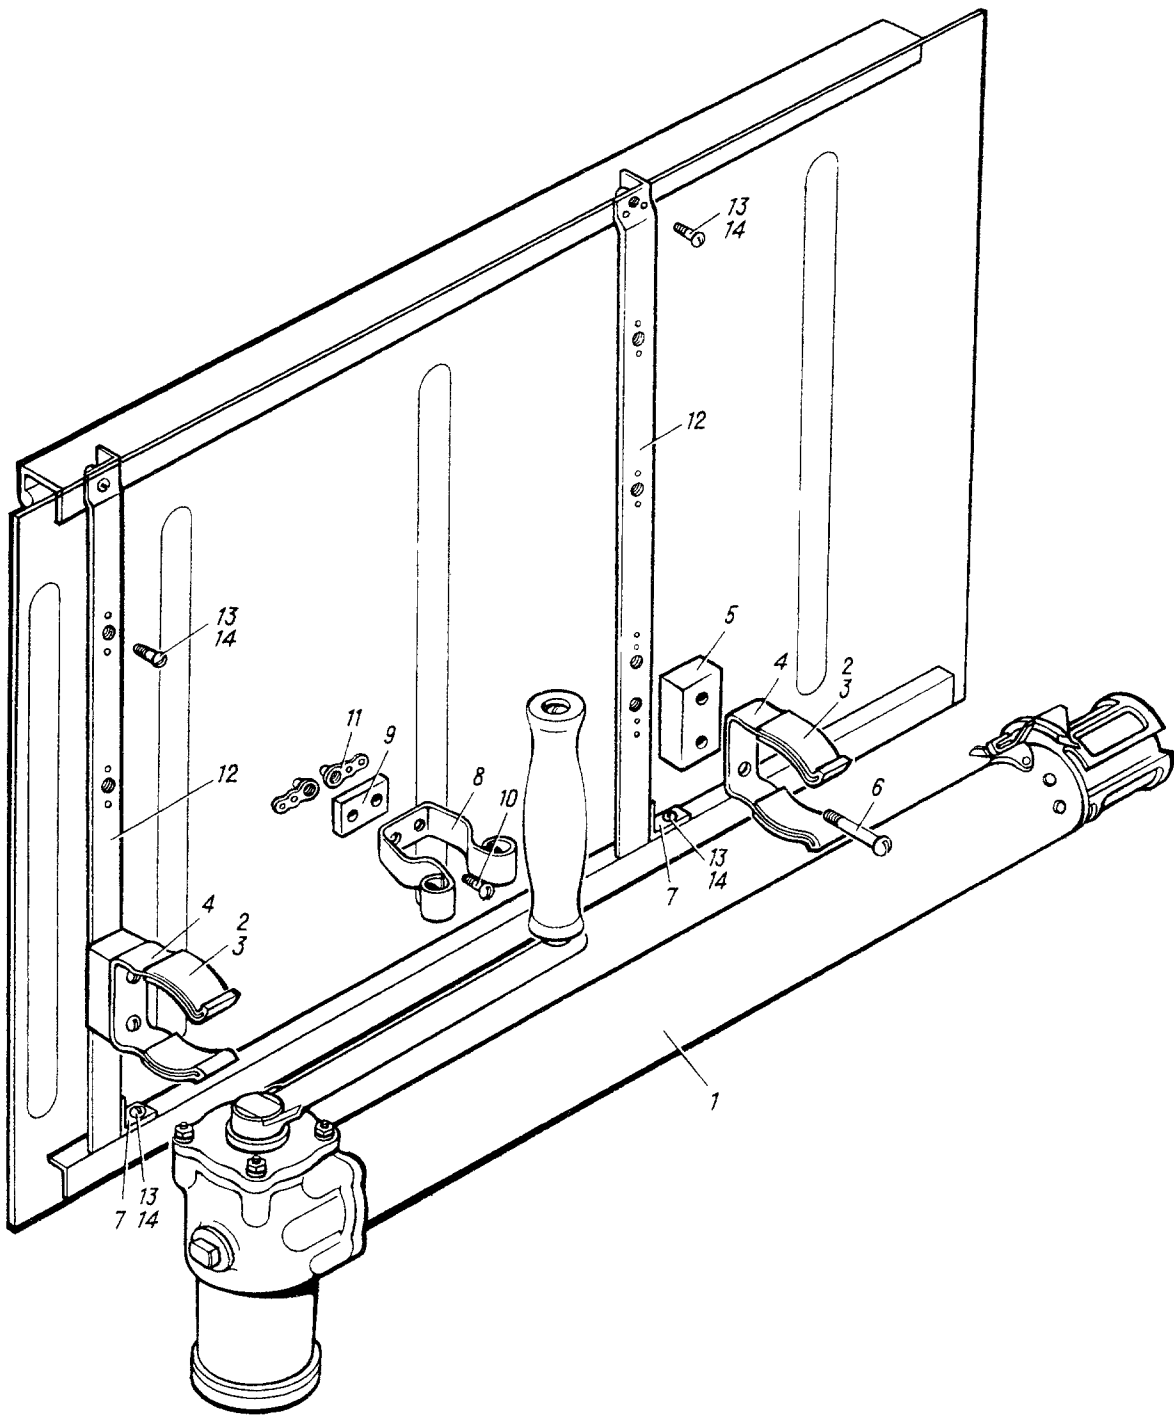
УСТАНОВКА КОЛОНКИ РУЧНОГО ПРИВОДА
